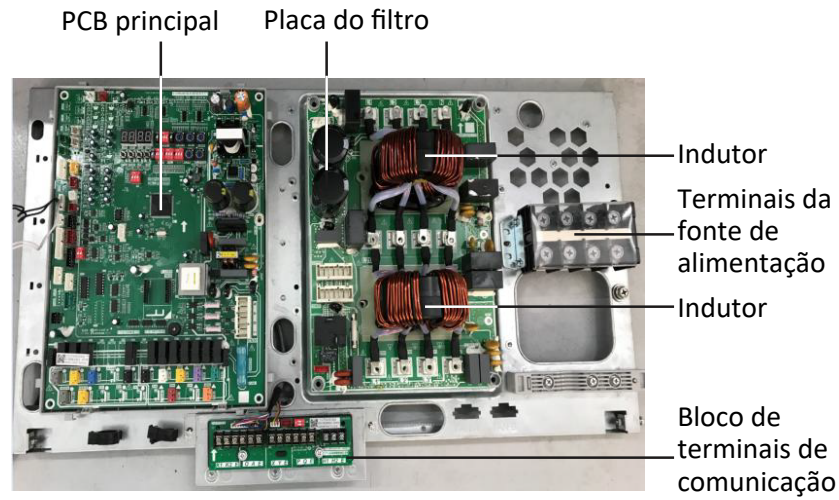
Camada superior de 20-32 HP da caixa de controle elétrico Placa do filtro da PCB principal
